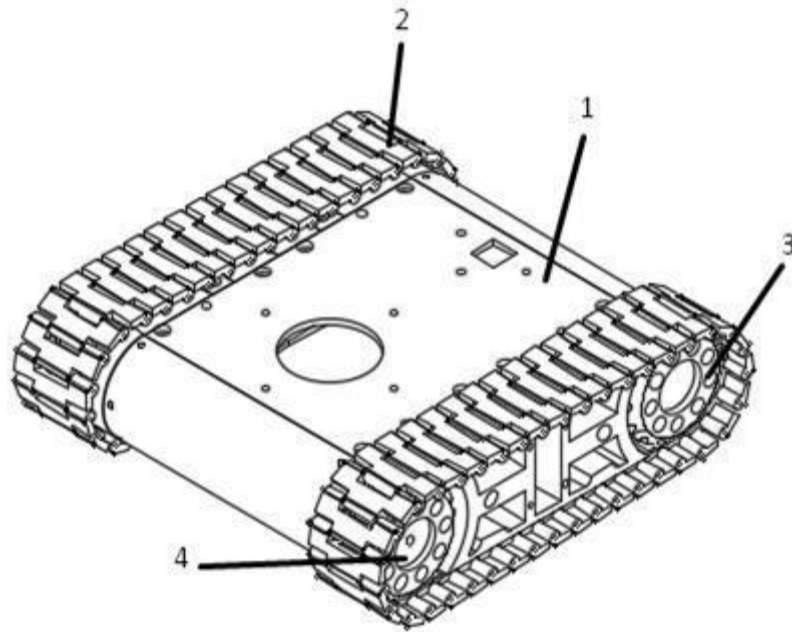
Гусенична платформа: 1- корпус, 2 - гусениця, 3 - ведений каток, 4 -ведучий каток
